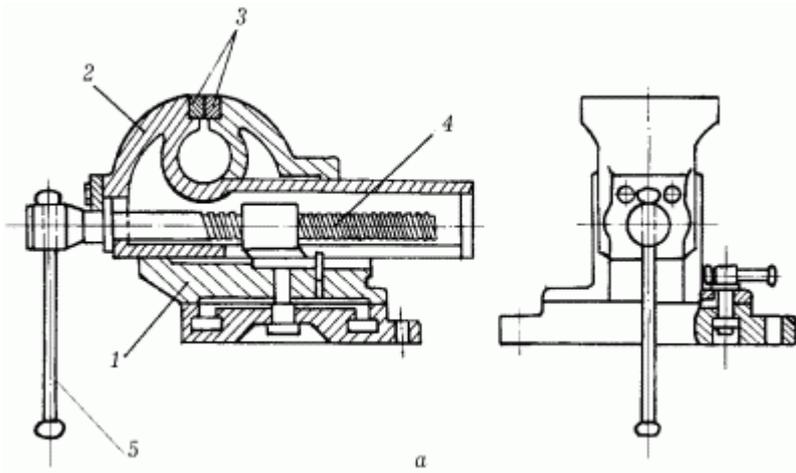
Зажимные приспособления: а – параллельные тиски: 1 – корпус; 2 – подвижная губка; 3 – пластины с насечками; 4 – винт; 5 – рукоятка винта.
